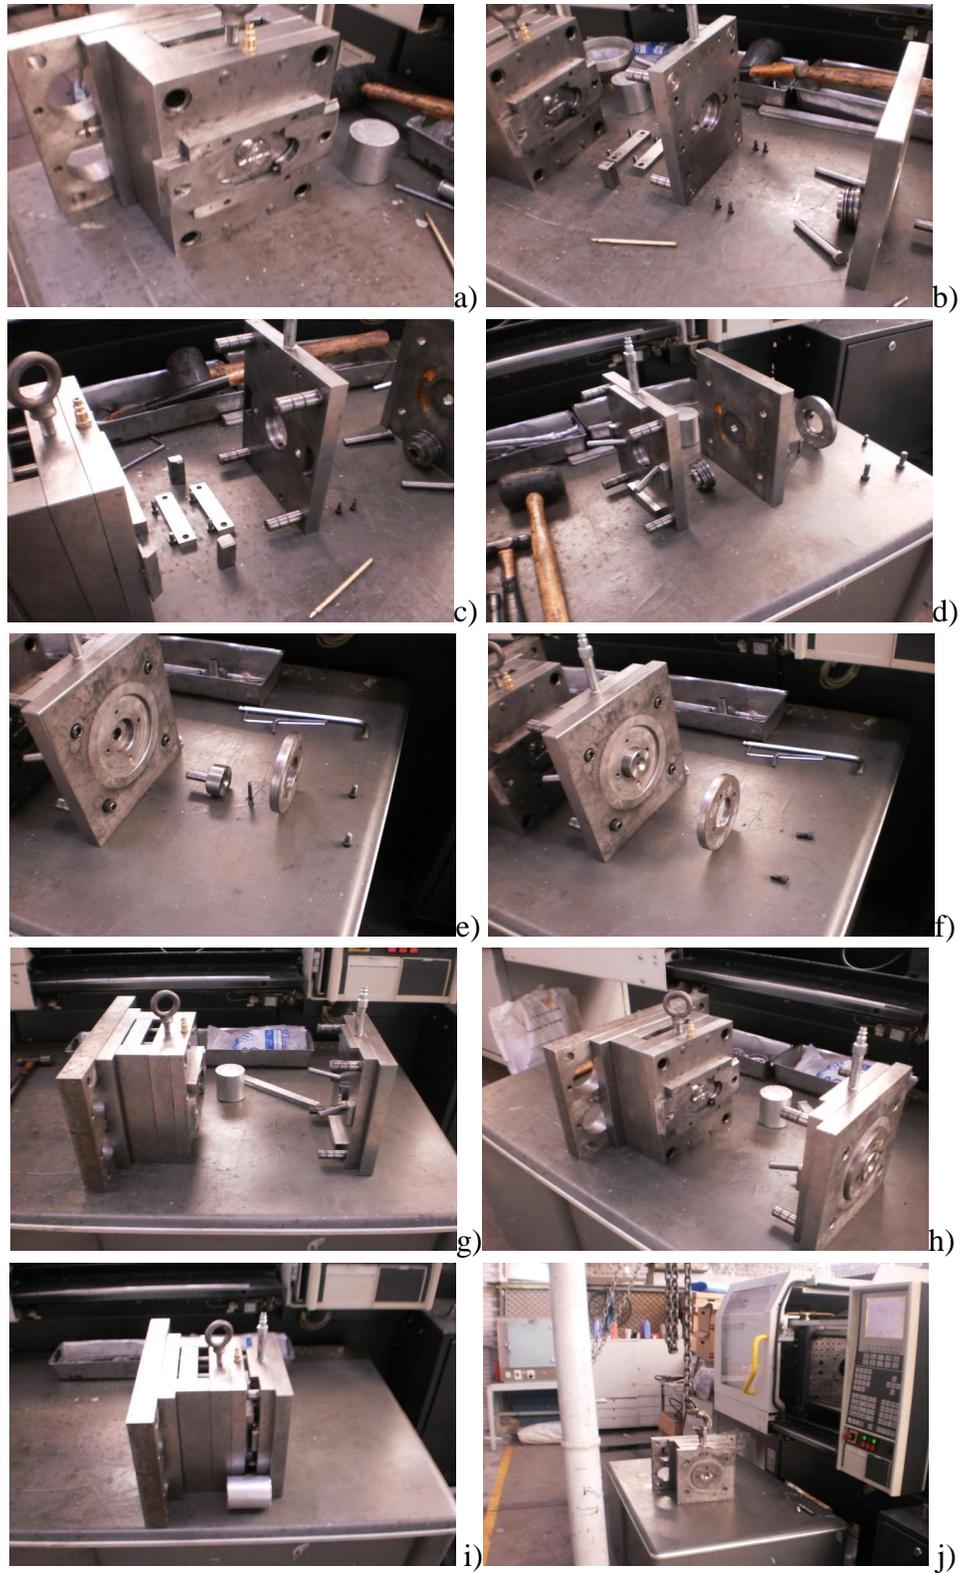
Procedimiento de ensamblado de los componentes del molde para la fabricación de la pieza base.
